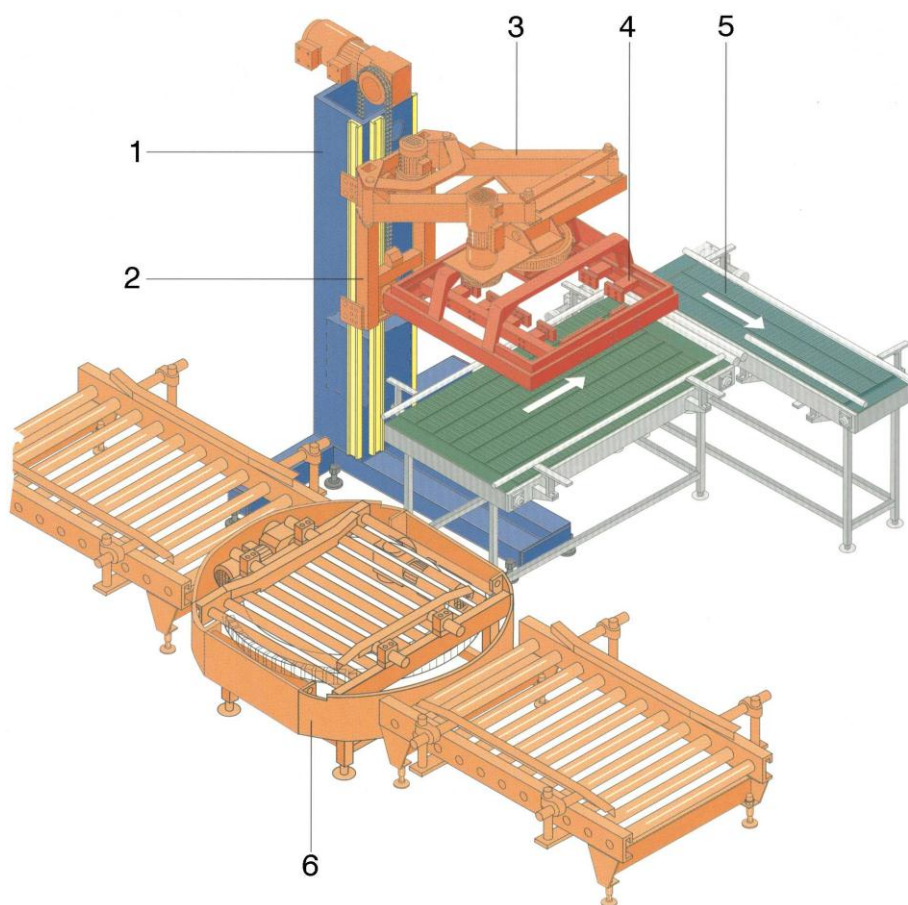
Instalație de paletizat tip Innopal: 1 – cadrul mașinii; 2 – mecanism de ridicare; 3 – mecanism pivotant pentru capul de încărcare; 4 – dispozitiv de prindere;
